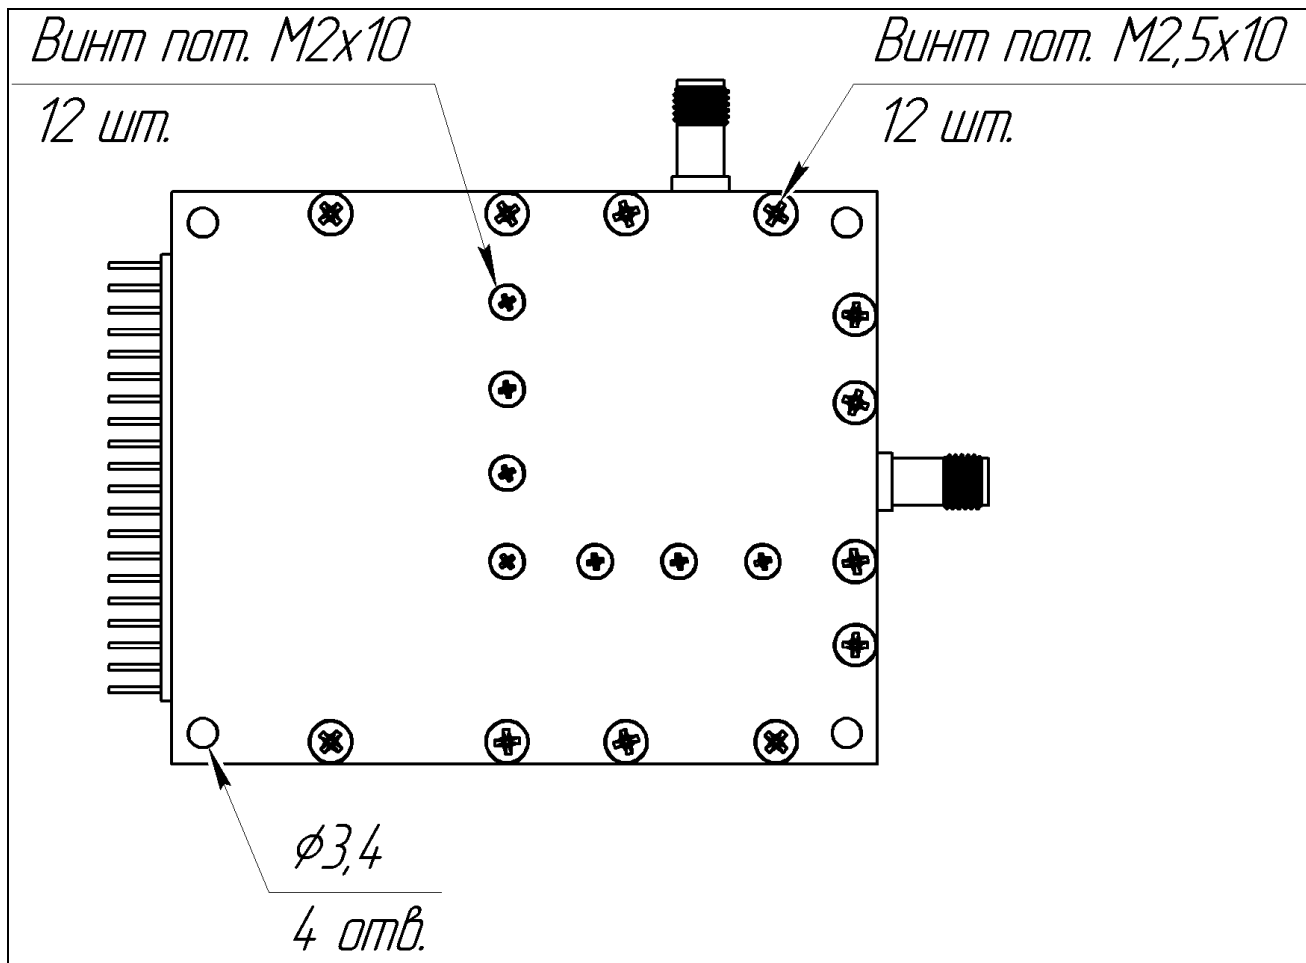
Расположение резьбовых соединений на корпусе синтезатора.
